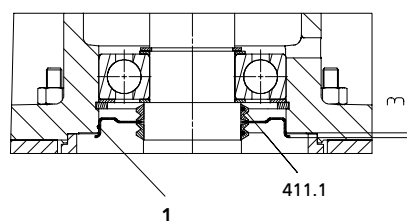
Уплотнение вала для узла вала 25 и узла вала 35
